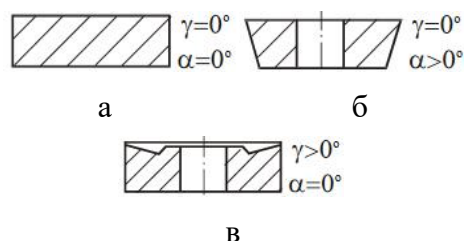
Геометрические параметры твердосплавных СМП. а – негативных; б – позитивных; в – негативно-позитивных
